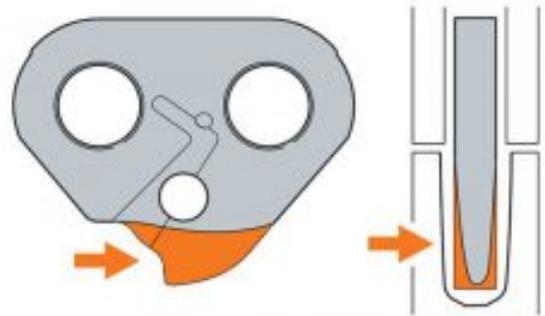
Износ боковых поверхностей носиков всех ведущих звеньев, закругление вершин
